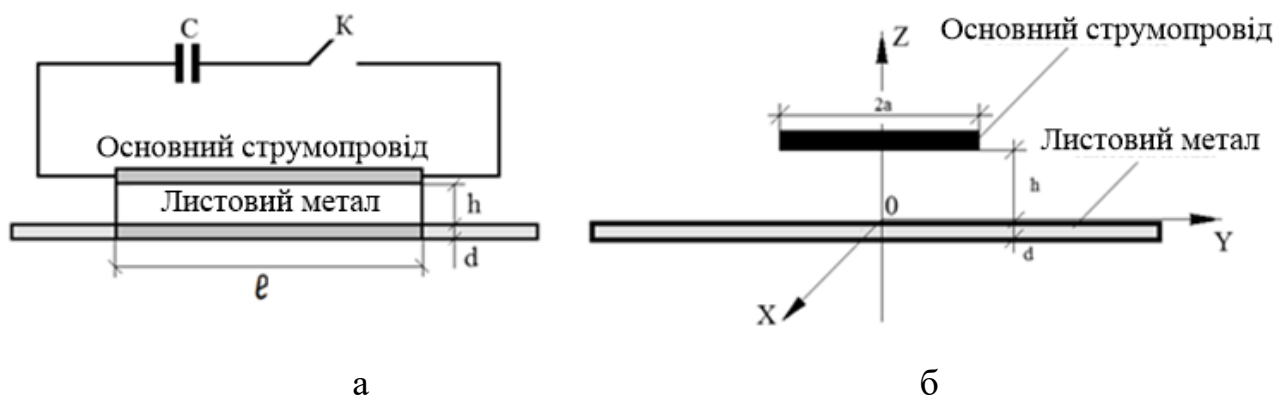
Принципова схема: а) електрична схема заміщення; б) основний струмопровід – металева полоса, заготовка – металевий лист
